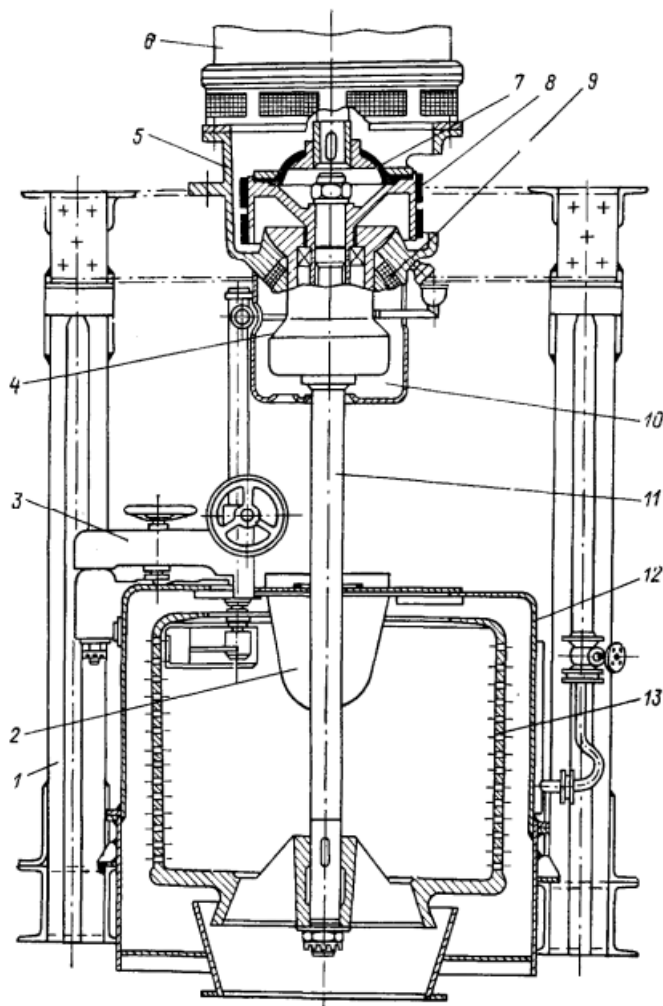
Підвісна центрифуга ФПН 1001У-1: 1 — металоконструкція; 2 — лоток; 3 — механізм зрізування осаду; 4 — корпус підшипників; 5 — корпус приводу; 6 — електродвигун; 7 — муфта; 8 — гальмо; 9 — амортизатор; 10 — привід; 11 — вал; 12 — кожух з кришкою; 13 — ротор
